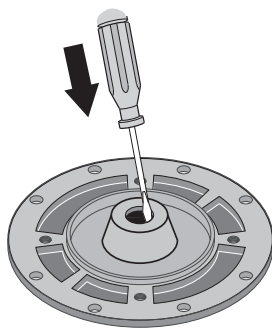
RETIRER EN APPUYANT SUR LE JOINT
